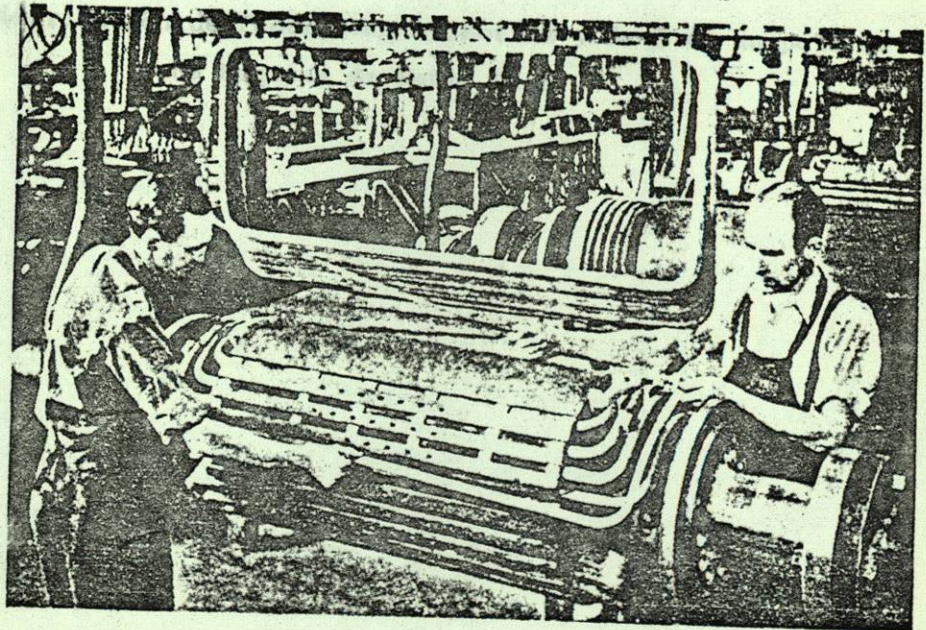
Montando el Devanado Concéntrico en un Rotor Cilíndrico
